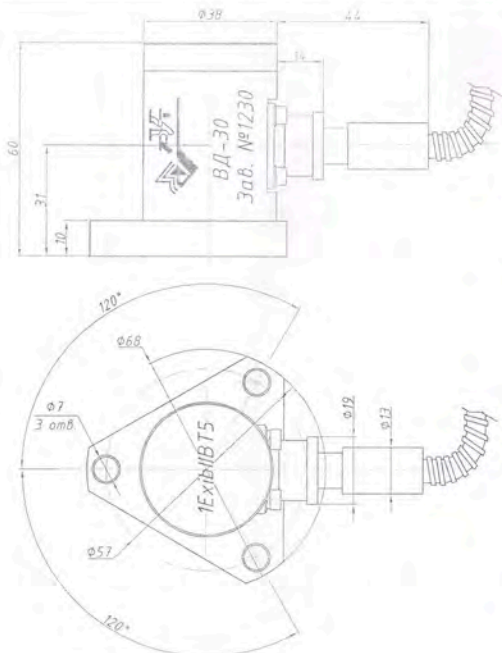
Габаритные и установочные размеры ВД-30.01-3
